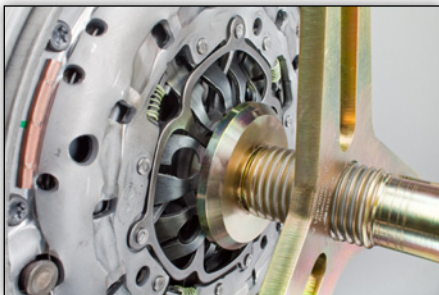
Tellerfeder durch Lösen der SAC-Werkzeugspindel entspannen und Werkzeug mit Stehbolzen abbauen
